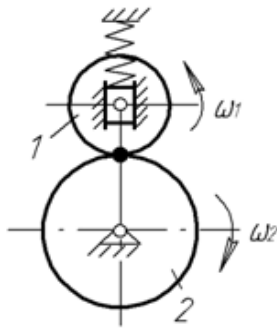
Фрикційний механізм з циліндричними котками
